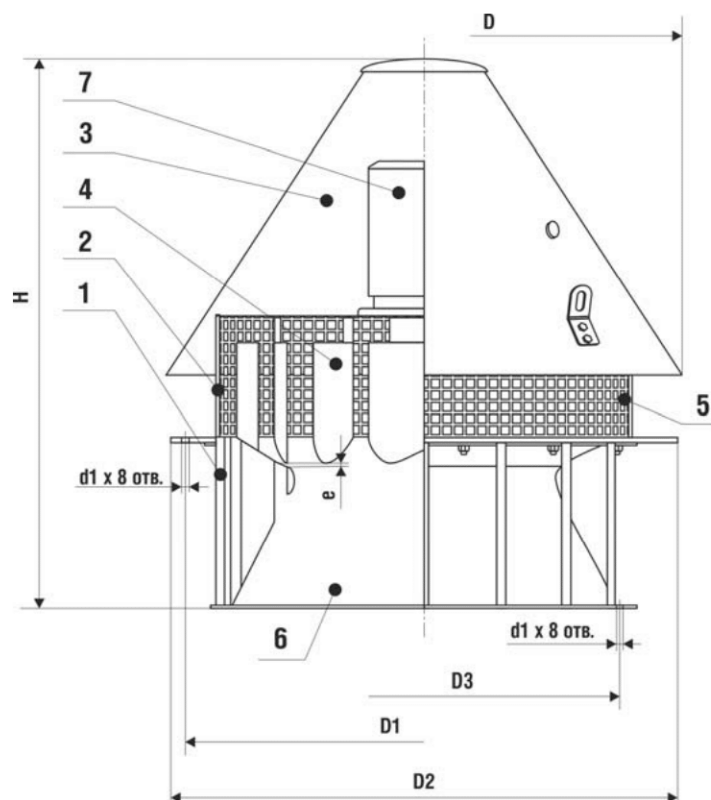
Габаритный чертеж вентиляторов ВКРМ
